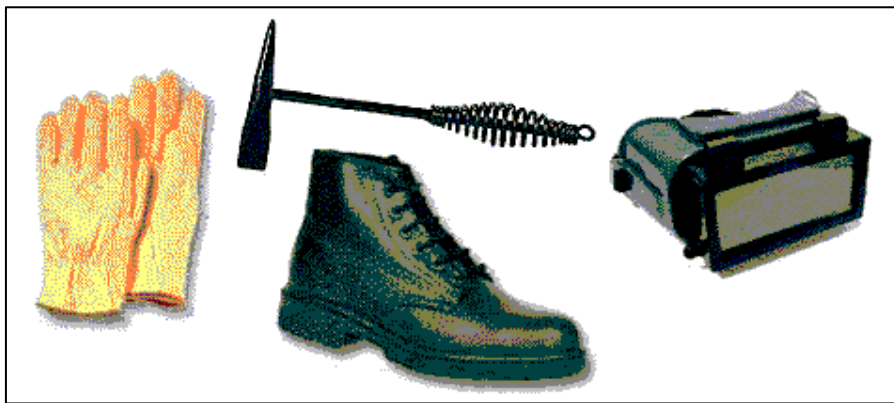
Seguridad en Corte y Soldadura Acetilénica
